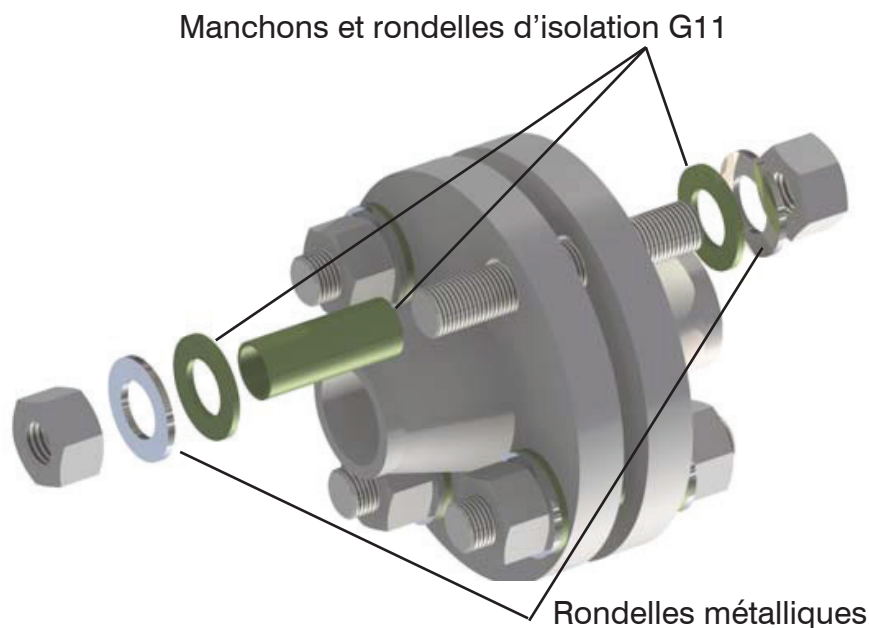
Ordre d'assemblage de rondelle, boulon et goujon
